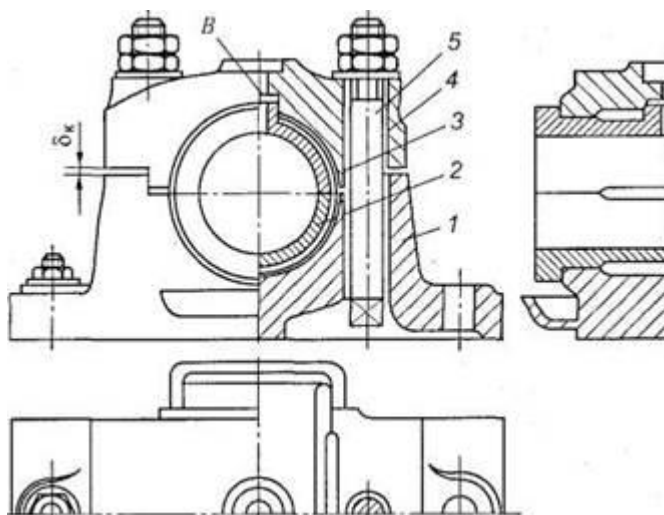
Разъемный подшипник скольжения: 1 — станина; 2, 3 — вкладыши (полукольца); 4 — крышка; 5 — болт
